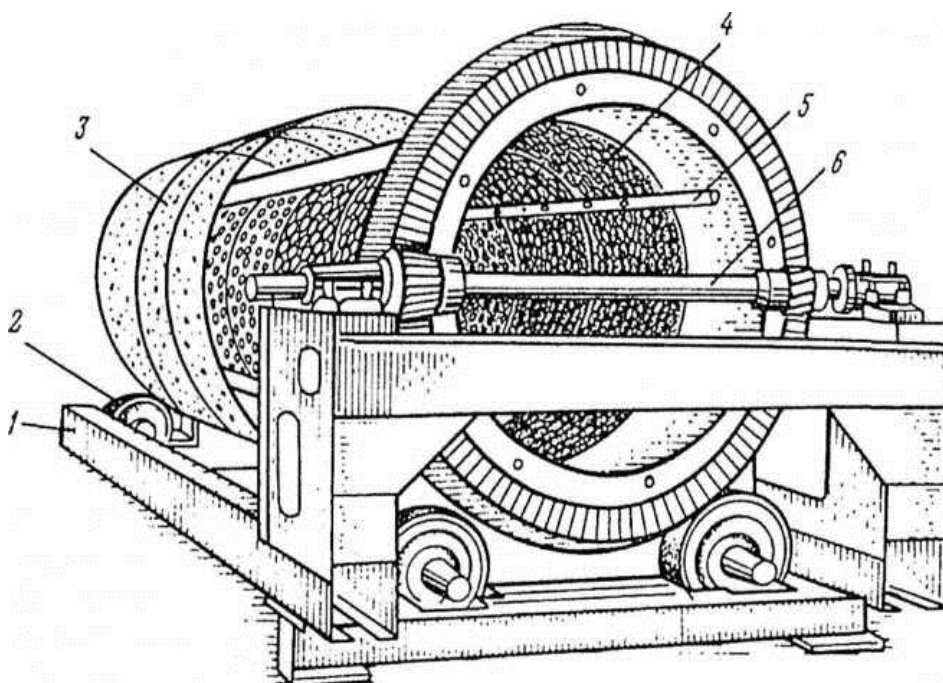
Гравимойка-сортировка: 1 — рама; 2 — опорный ролик; 3 — наружный перфорированный барабан; 4 — внутренний перфорированный барабан; 5 — водовод; 6 — приводной вал
